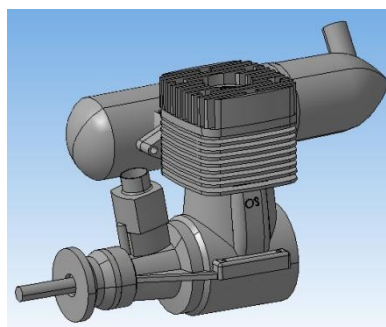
Схема двигатель OS-MAX BGX RING.
